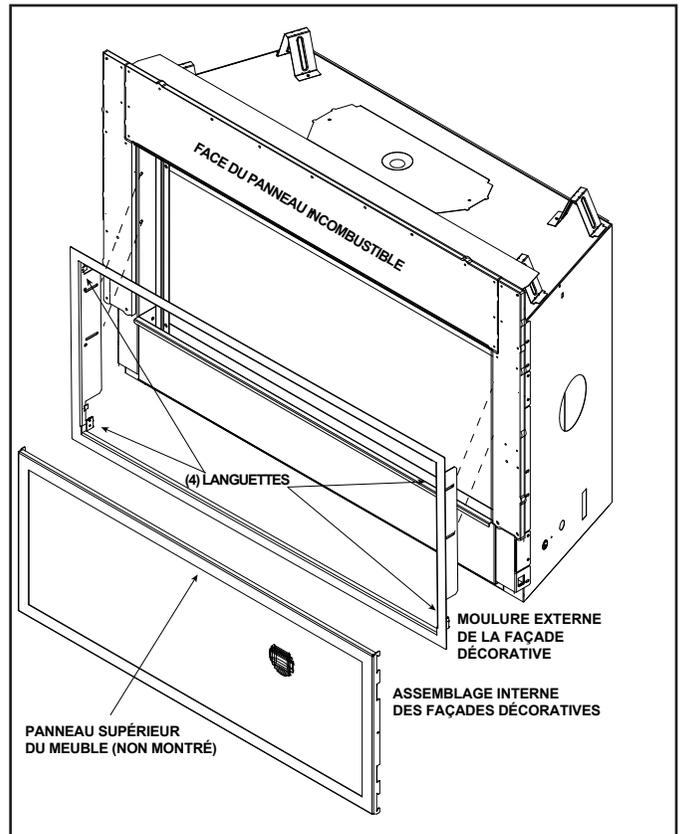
Installation de la façade CFT avec la moulure externe de la façade décorative
